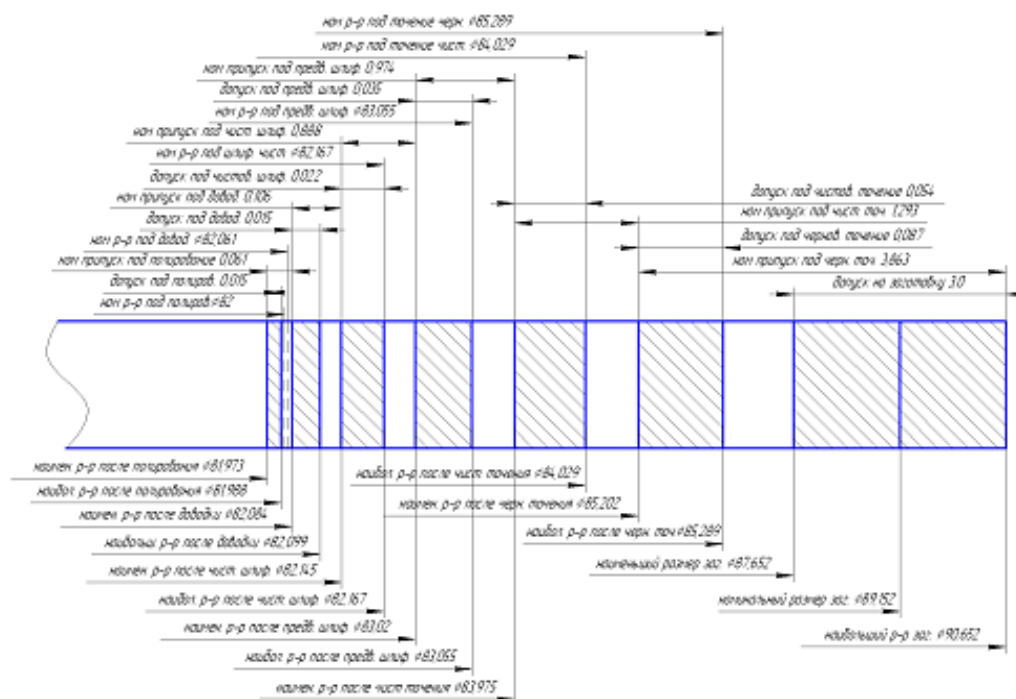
Схема расположения припусков и допусков при обработке поверхности Ø82g5
